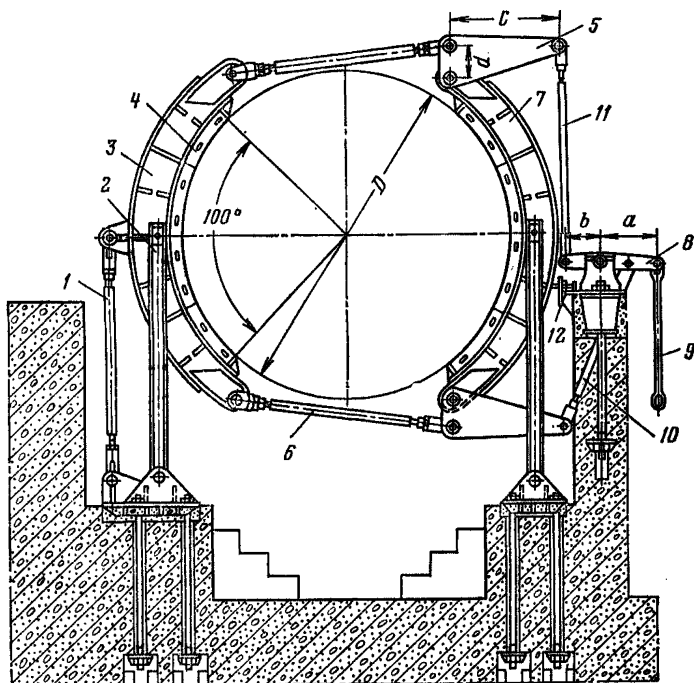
Схема исполнительного органа тормоза подъемных машин НКМЗ (I типа); 1 — винтовая стойка; 2 — стойка; 3 и 7 — тормозные балки; 4 — тормозные колодки; 5 и 8 — рычаги; 6, 9, 10 и 11 — тяги; 12 — упорный винт
